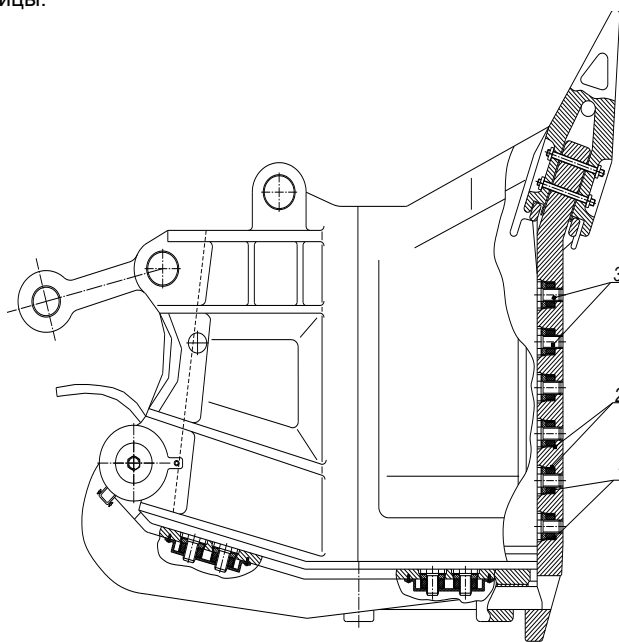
Ковш экскаватора с пакетными пьезокерамическими преобразователями
